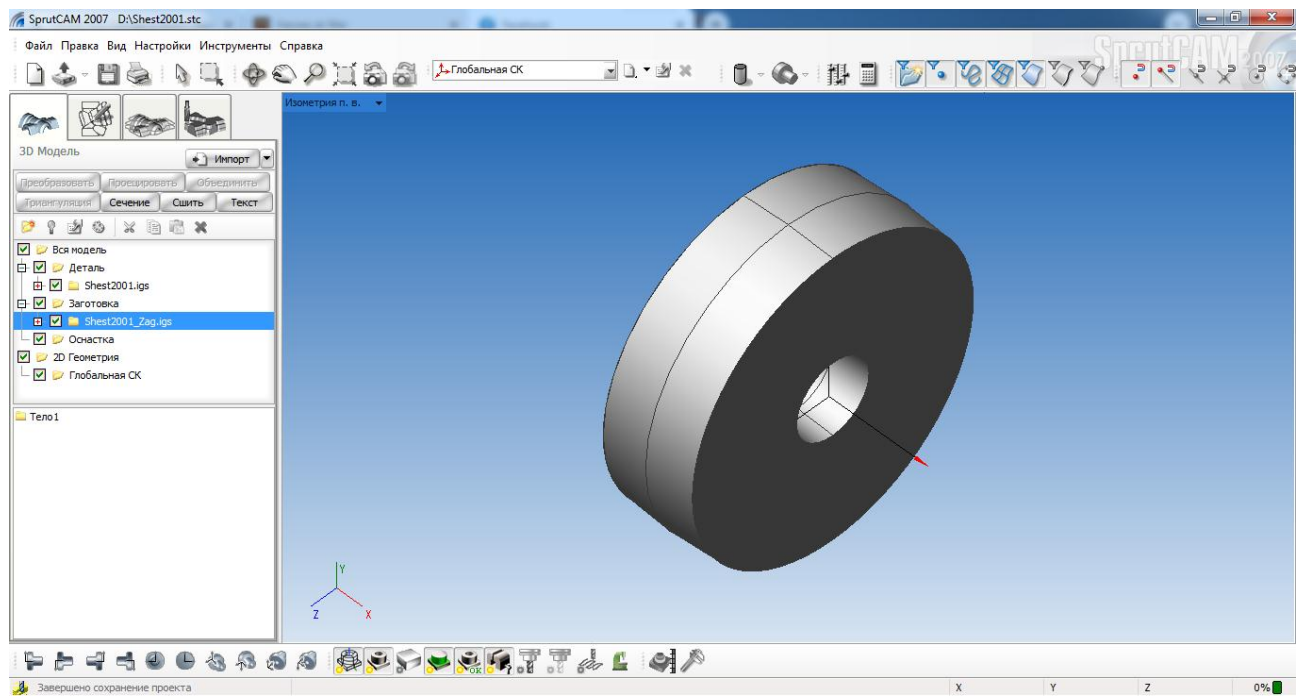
3D-моделі заготовки та деталі, імпортовані у систему SprutCAM
